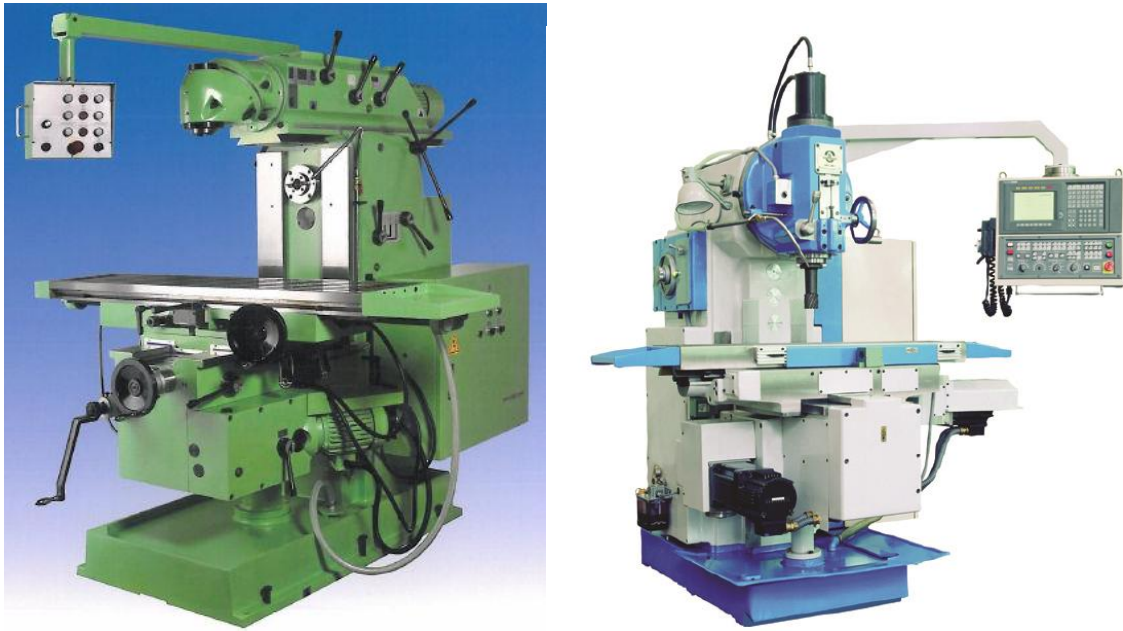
a) Fraiseuse universelle b) Fraiseuse à commande numérique
